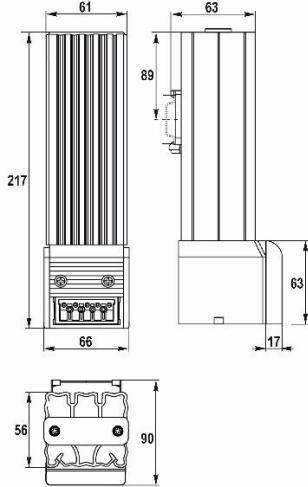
б – Общий вид и габаритные размеры нагревателей UNISPLIT 402SXXX
